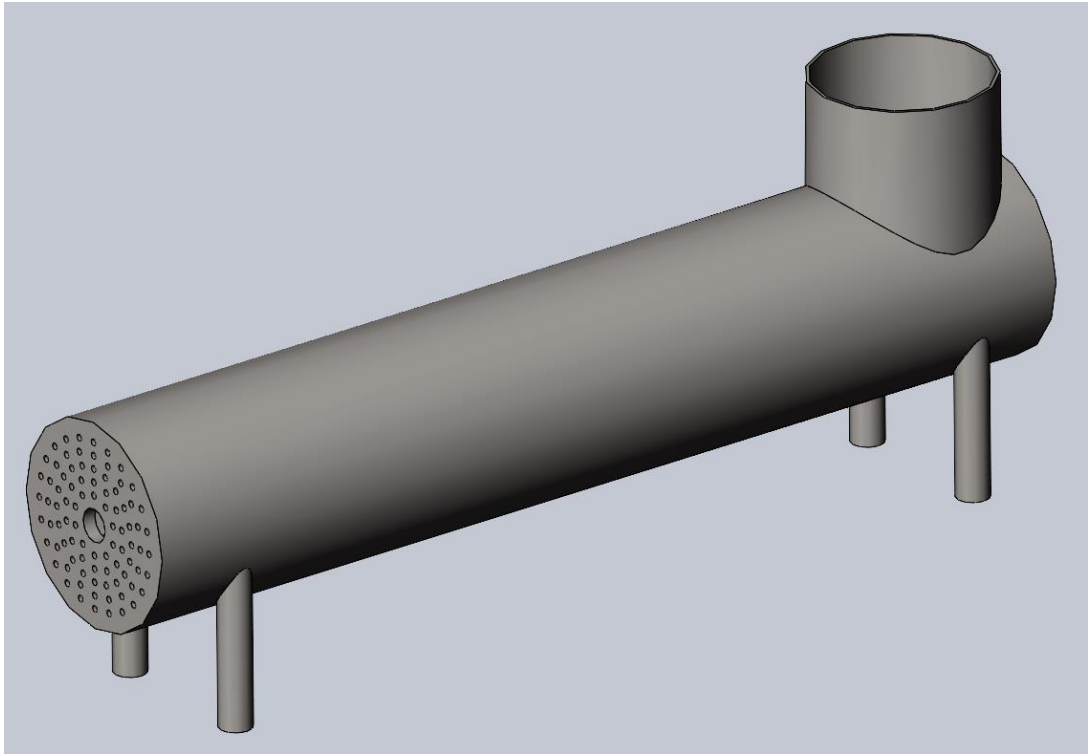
3-Д модель корпусу шнекової установки
